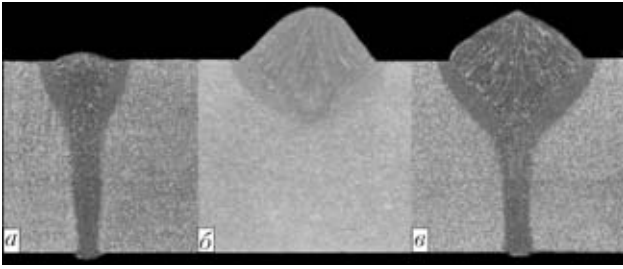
Макрошлифы сварных соединений, выполненных лазерной (а), дуговой (б) и гибридной лазерно-дуговой (в) сваркой
